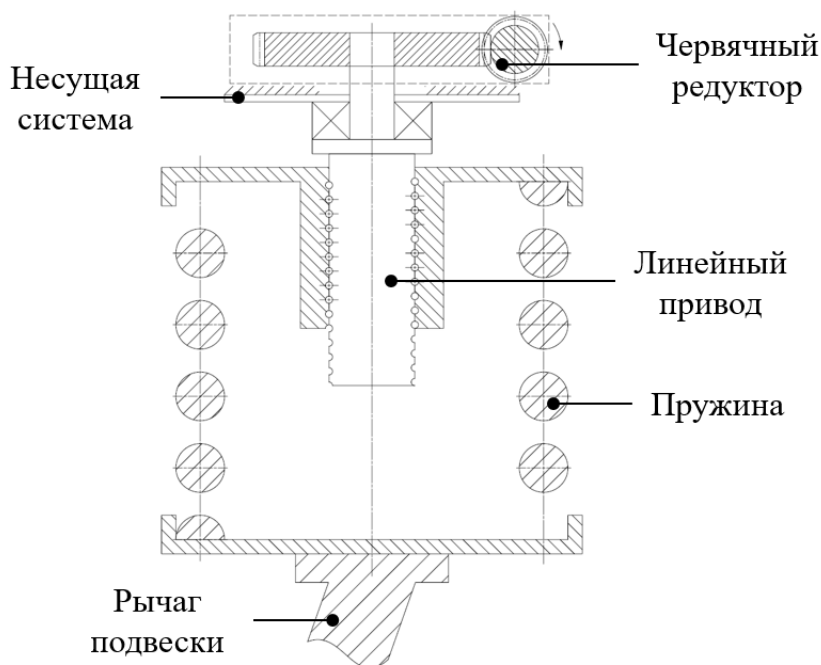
Схема устройства для управления положением корпуса электробуса и его расположения в подвеске
